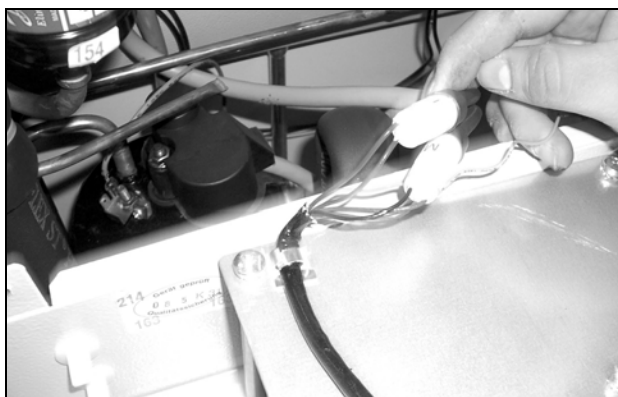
Zasunutí kabelu displeje zpět a protlačení průchodkou (1)
